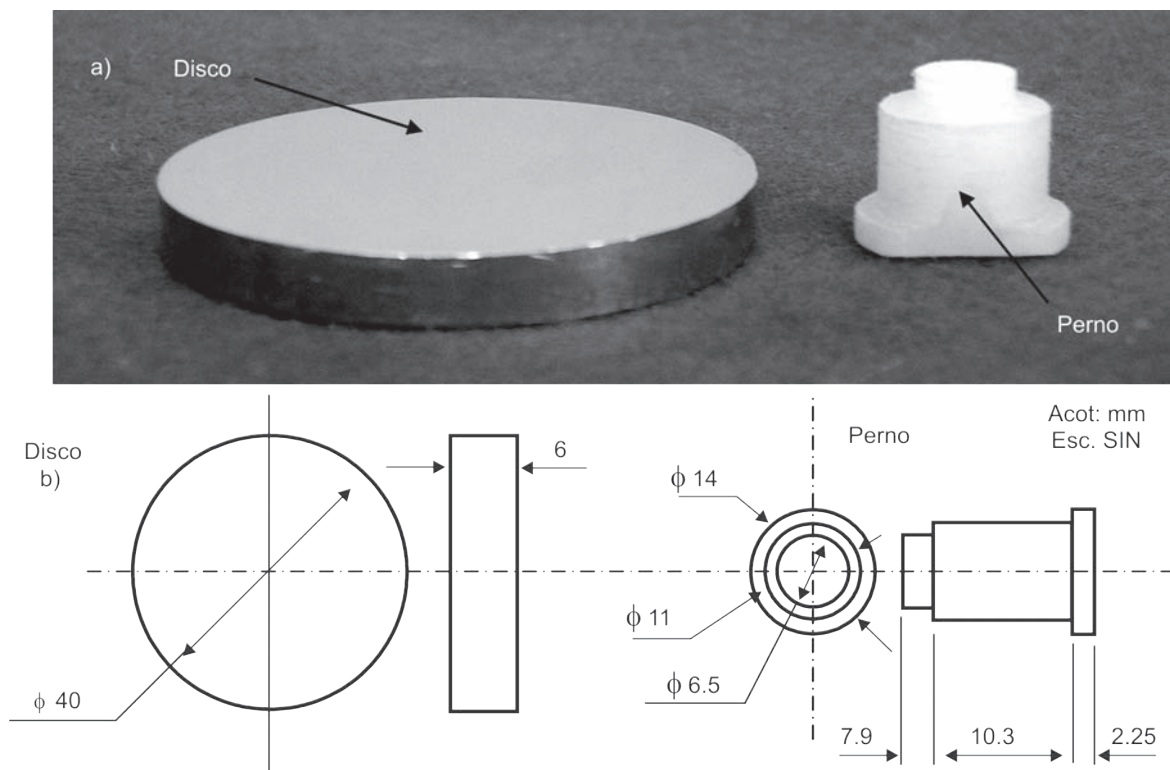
Probetas utilizadas. a) Fotografía; b) dimensiones en mm.
